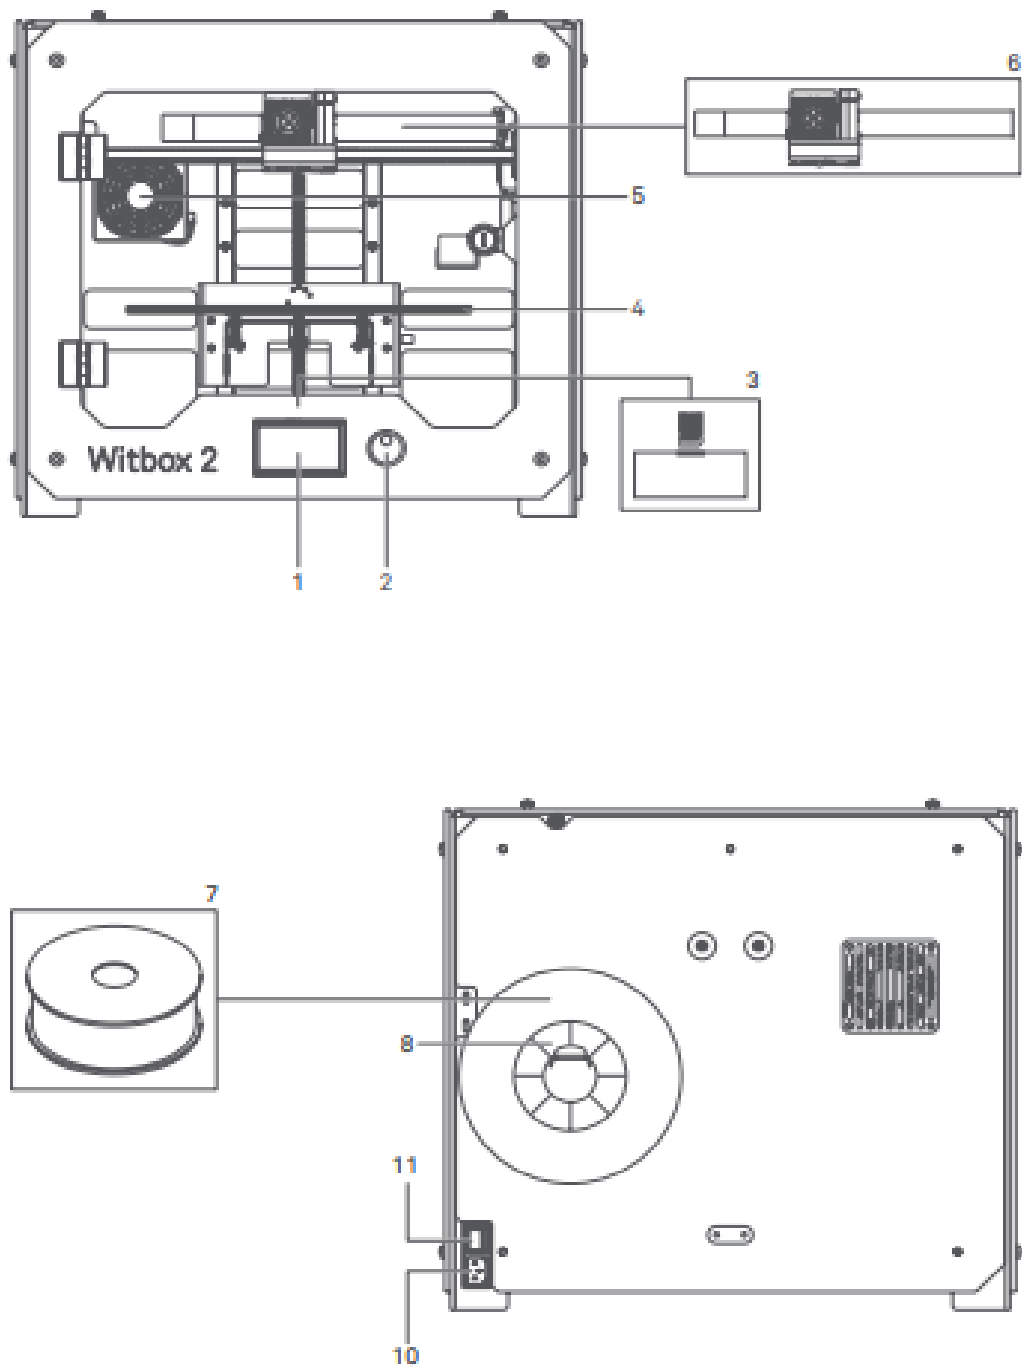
Основные части в 3D-принтере Witbox 2
